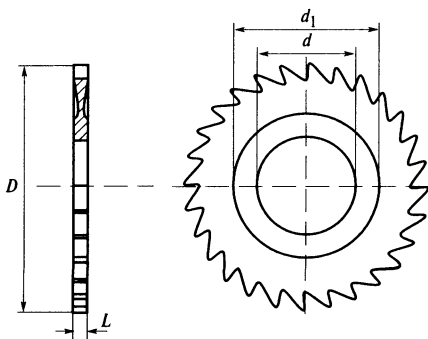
Металлические дисковые фрезы без бокового зазора с мелким зубом
